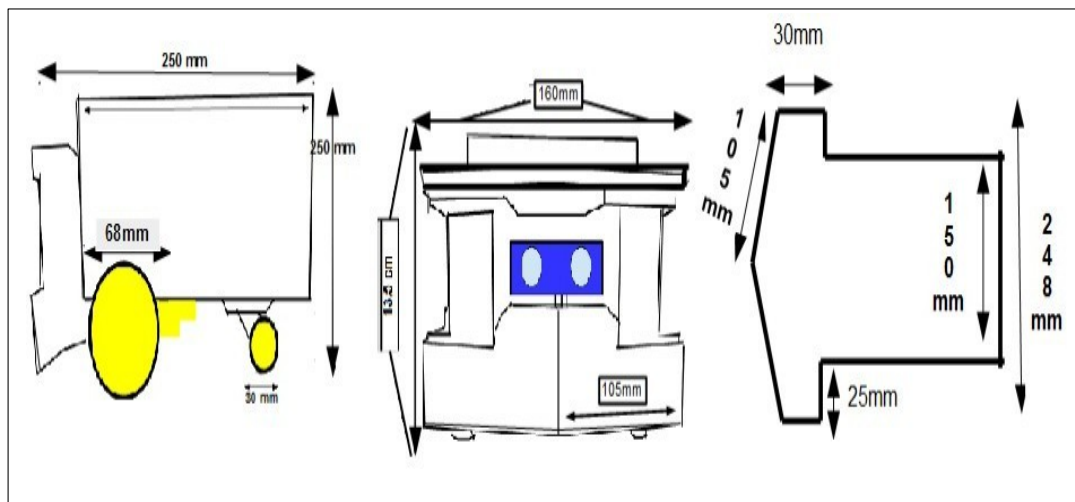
Desenho Técnico Do Carrinho Seguidor De Linha
